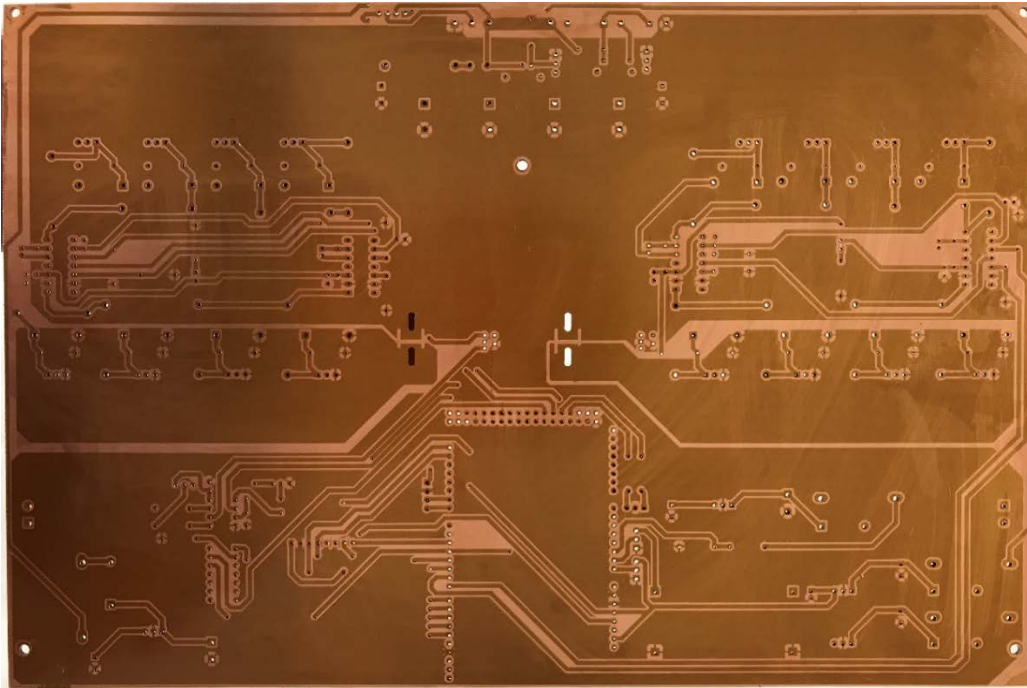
cara inferior de la PCB tras el proceso de insulado
